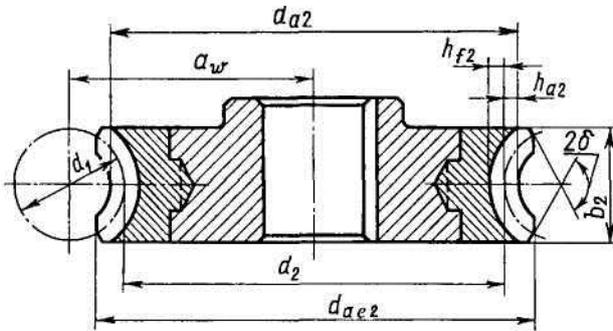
Основные размеры венца червячного колеса делительный и совпадающий с ним начальный диаметр
